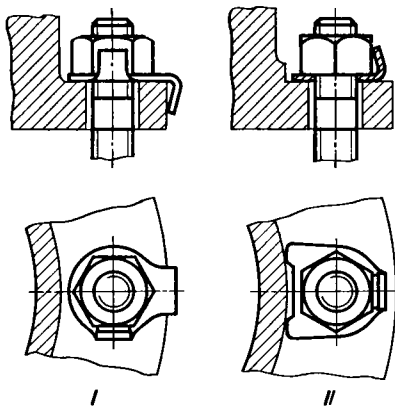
Установка стопорной шайбы на цилиндрическом фланце:
